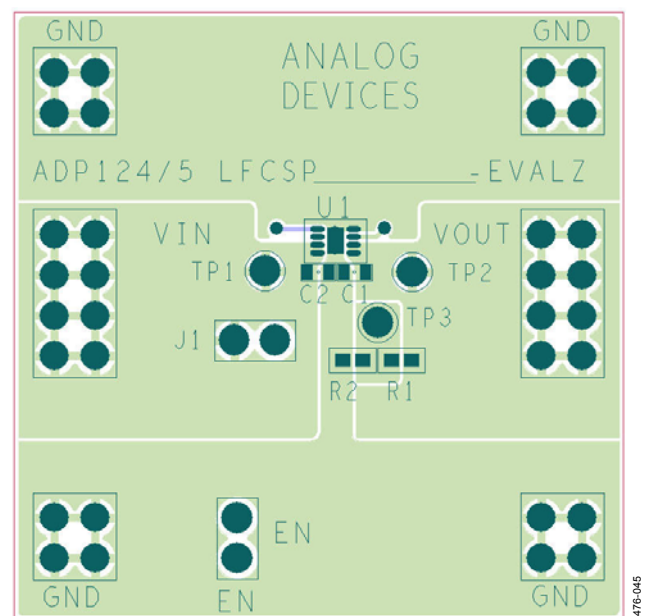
ADP124/ADP125 LFCSP の PCB レイアウト例
